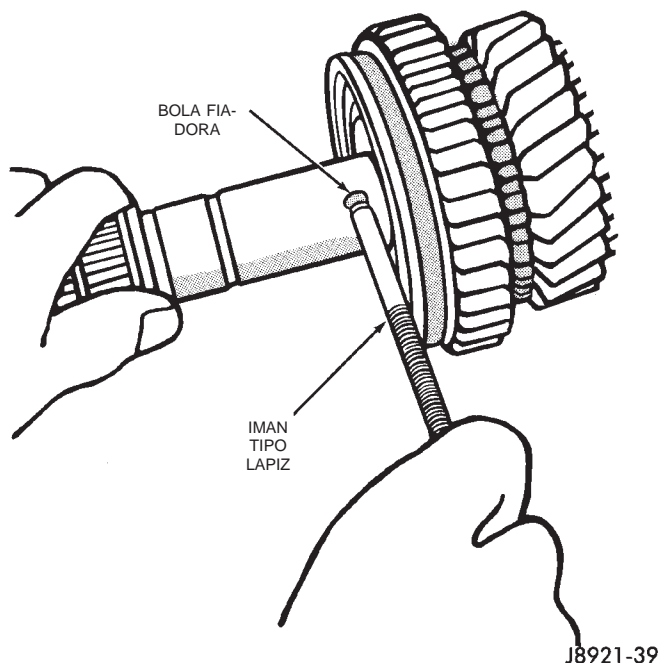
Desmontaje de bola fiadora de pista de rodamiento interior de cojinete de engranaje de primera velocidad
